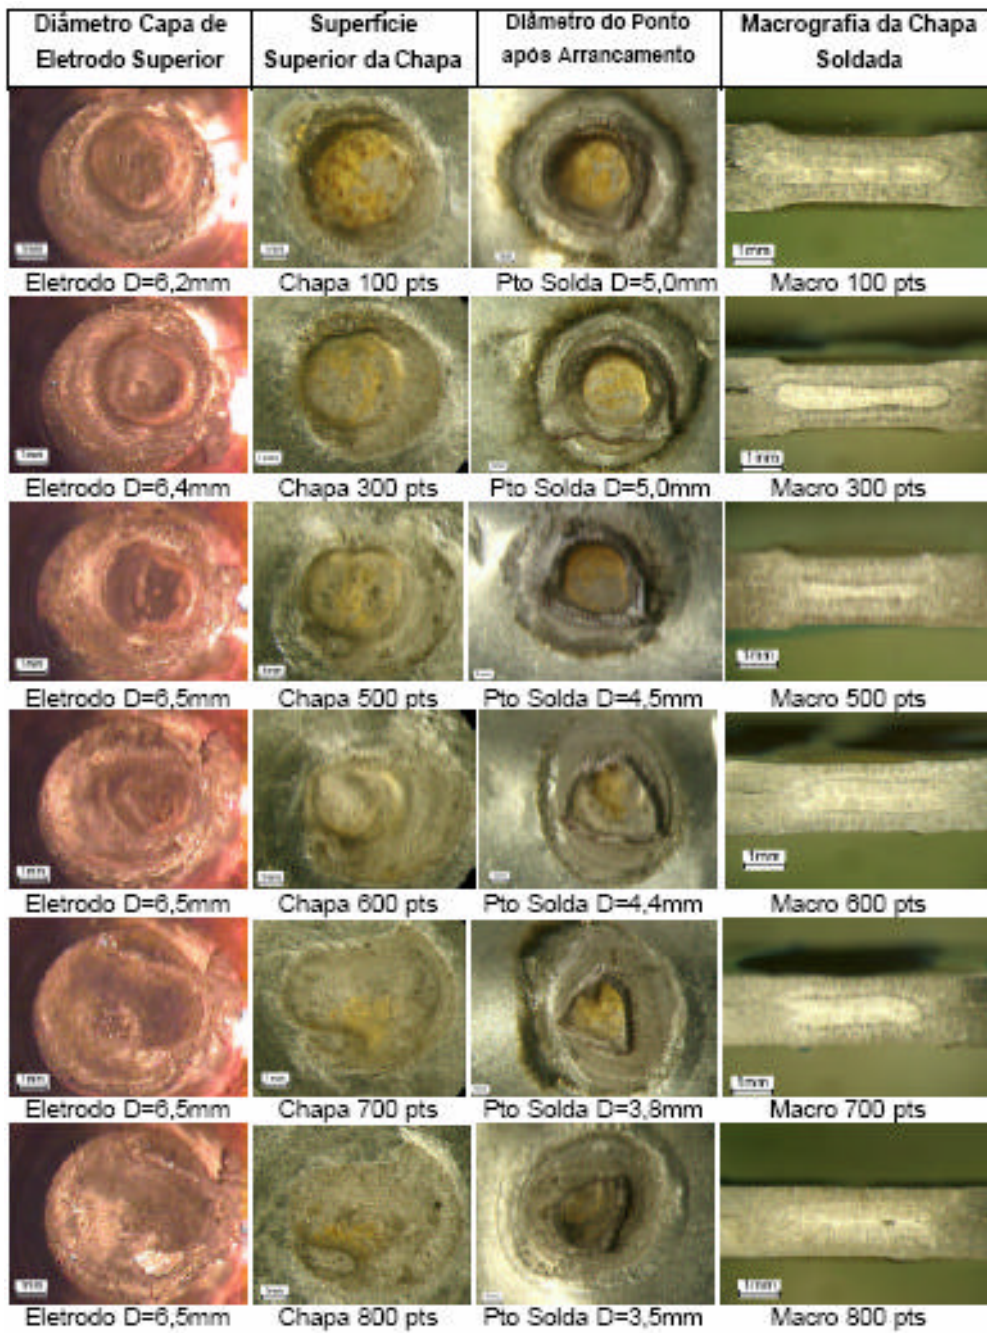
Pontos soldados com a capa de eletrodo C.
